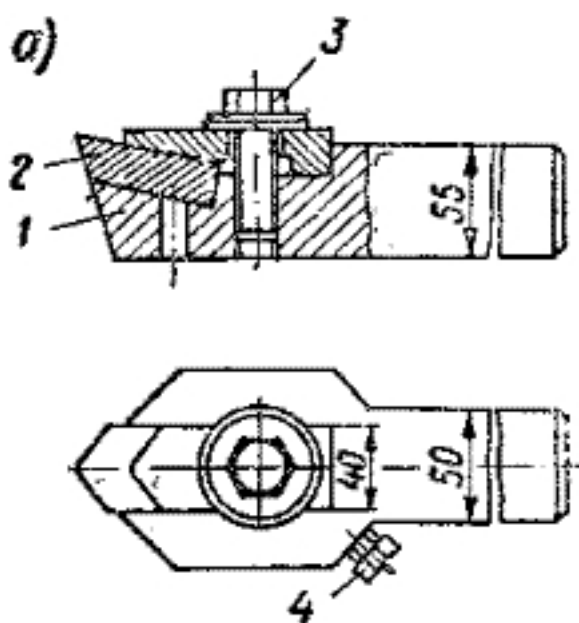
Многофлютовый резец с механическим креплением режущей пластинки.
